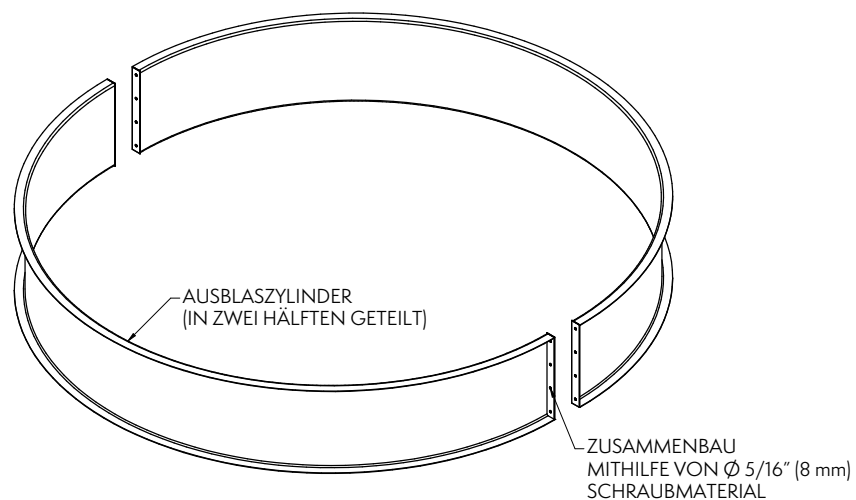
Geteilter Ventilatorzylinder für Transport in Container mit Standardhöhe
